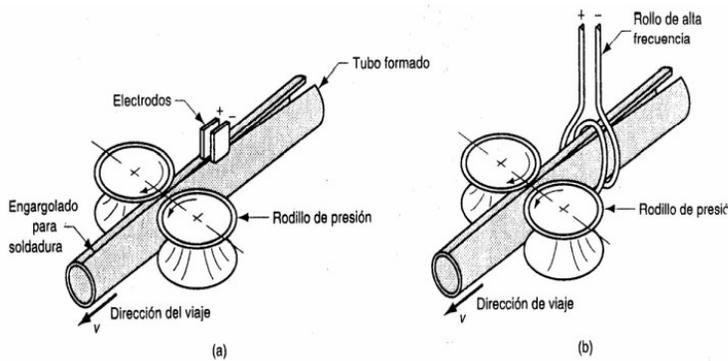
Soldadura de engargolados de tubos mediante; (a) soldadura por resistencia de alta frecuencia y (b) soldadura por inducción de alta frecuencia.
